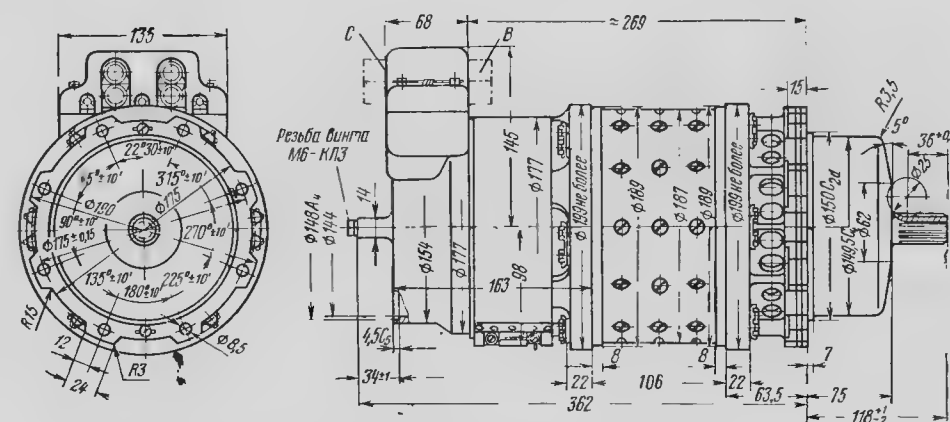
Габаритные размеры стартер-генератора СТГ-12ТМО-1000
